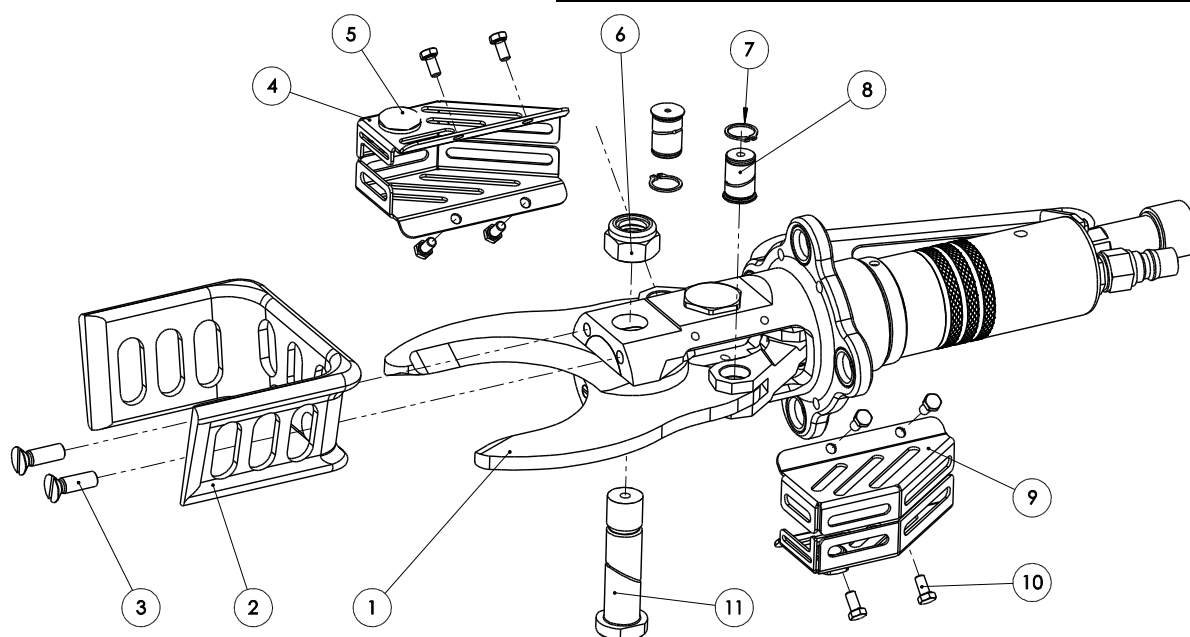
Explosionszeichnung (Beispiel Z079)
